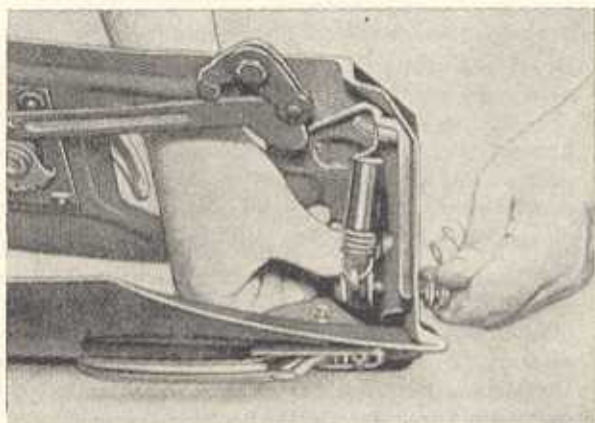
Einsetzen des Riegels mit Betätigungshebel
